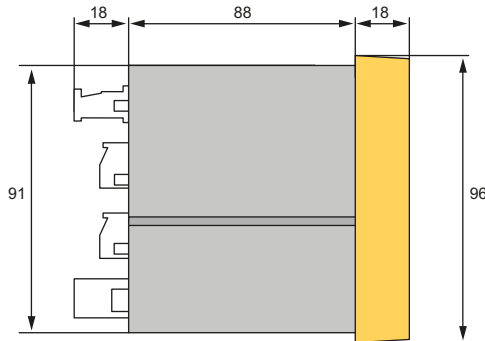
Maßbild PEM575 (Seitenansicht)
